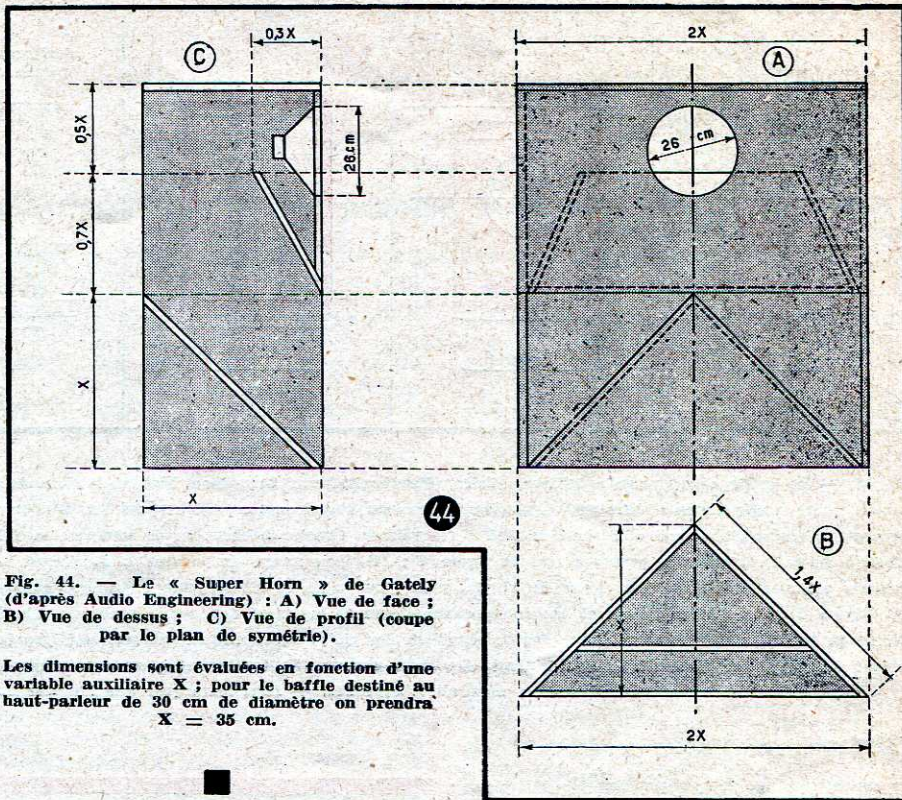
Le « Super Horn » de Gately (d'après Audio Engineering) : A) Vue de face ; B) Vue de dessus ; C) Vue de profil (coupe par le plan de symétrie).
